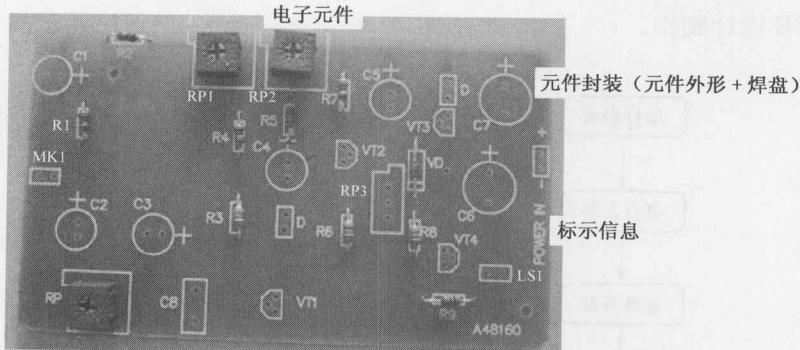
根据 PCB 图制作的 PCB 顶层（已经焊接了个别元件）
